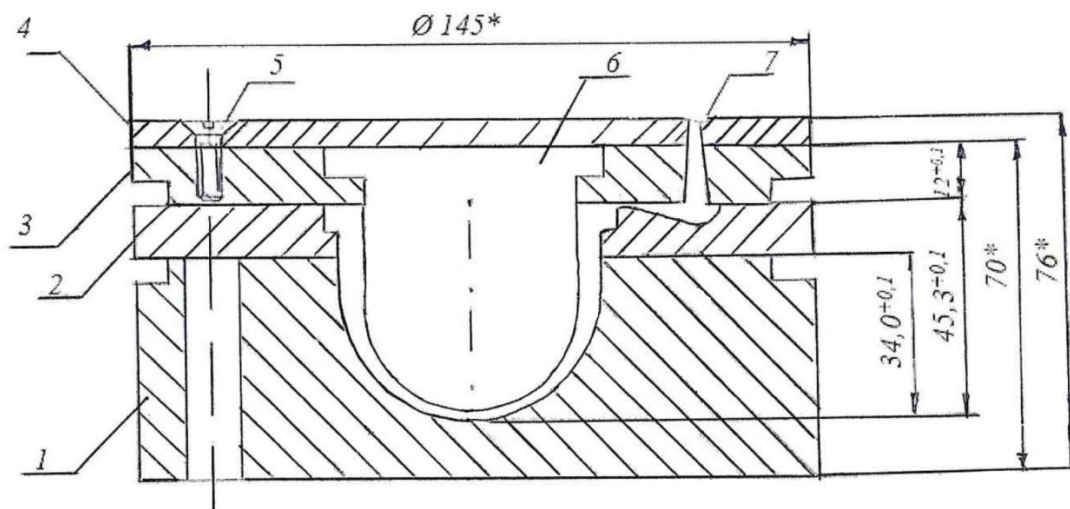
Пресс-форма для прессования корпусного элемента:
